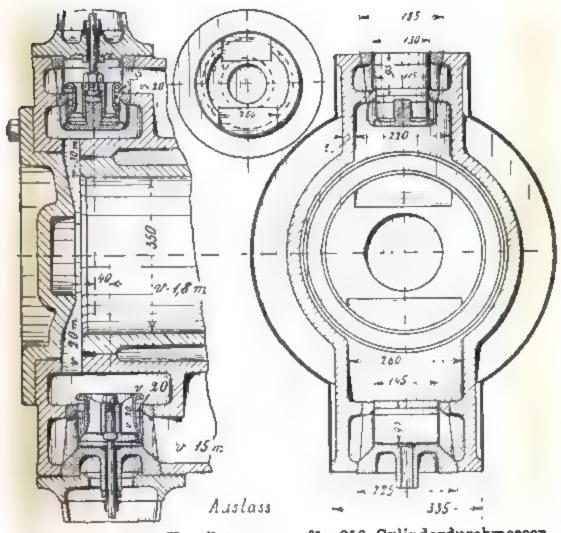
Ventilsteuerung für 350 Cylinderdurchmesser.
